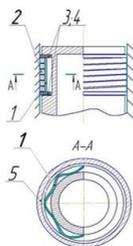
Принципиальная схема расположения поршня в цилиндре компрессора:
